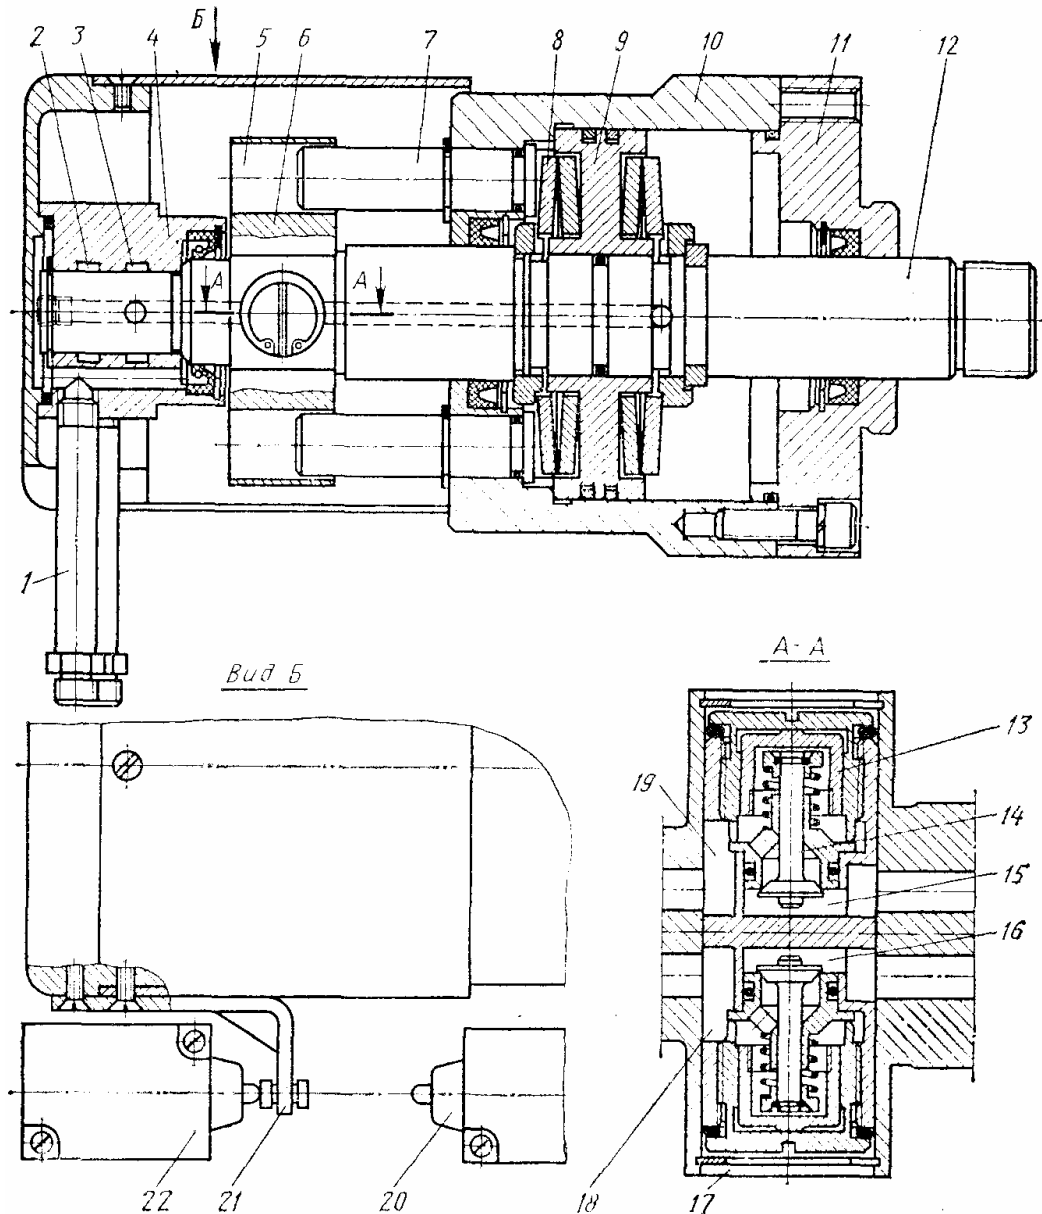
Конструкція гідроциліндра, що обертається, привода затискувального патрона для токарних верстатів
